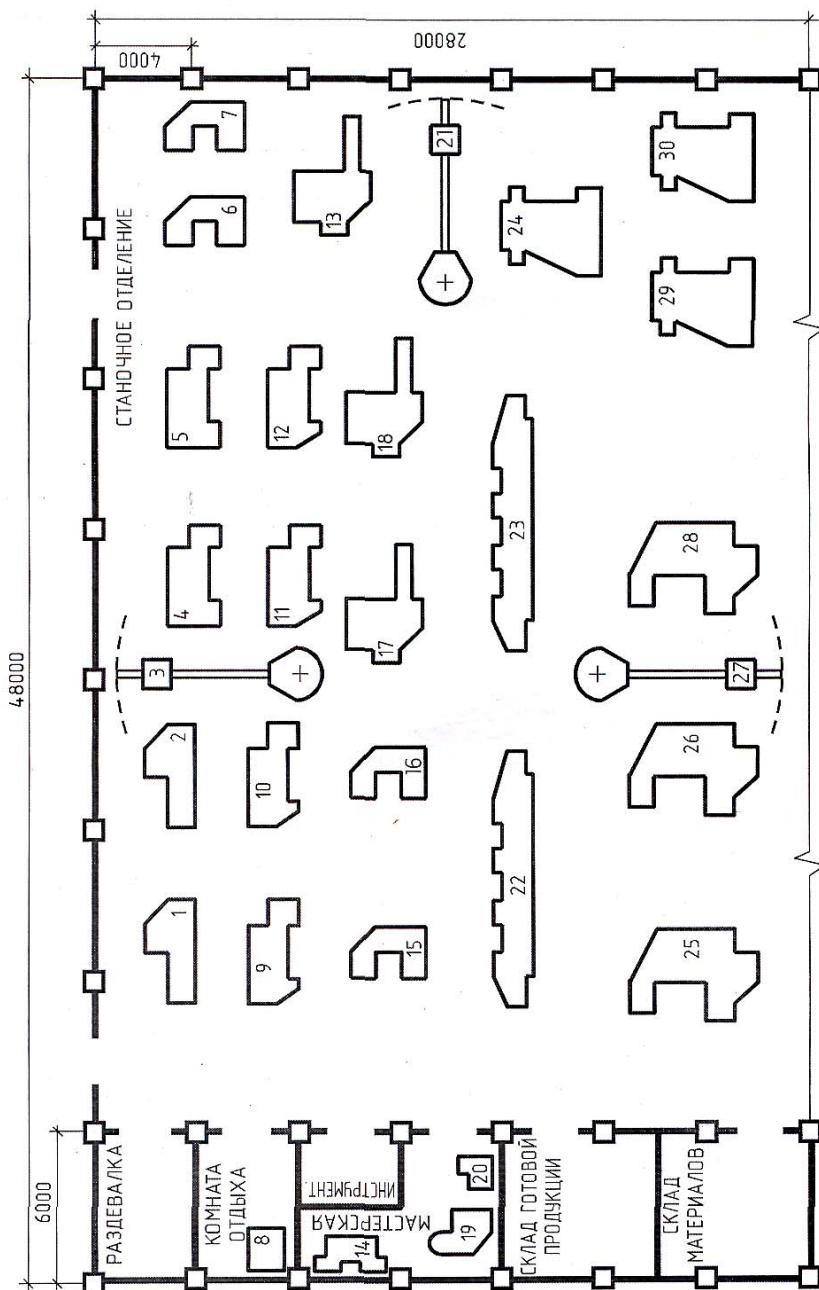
План расположения ЭО участка токарного цеха
